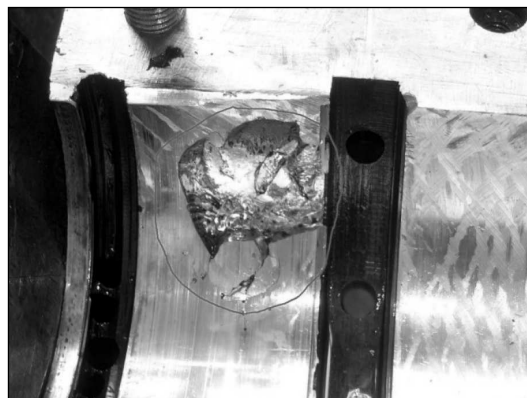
Разрушение баббитового слоя опорного подшипника центробежного нагнетателя ГПА №3 Валдайского ЛПУМГ
